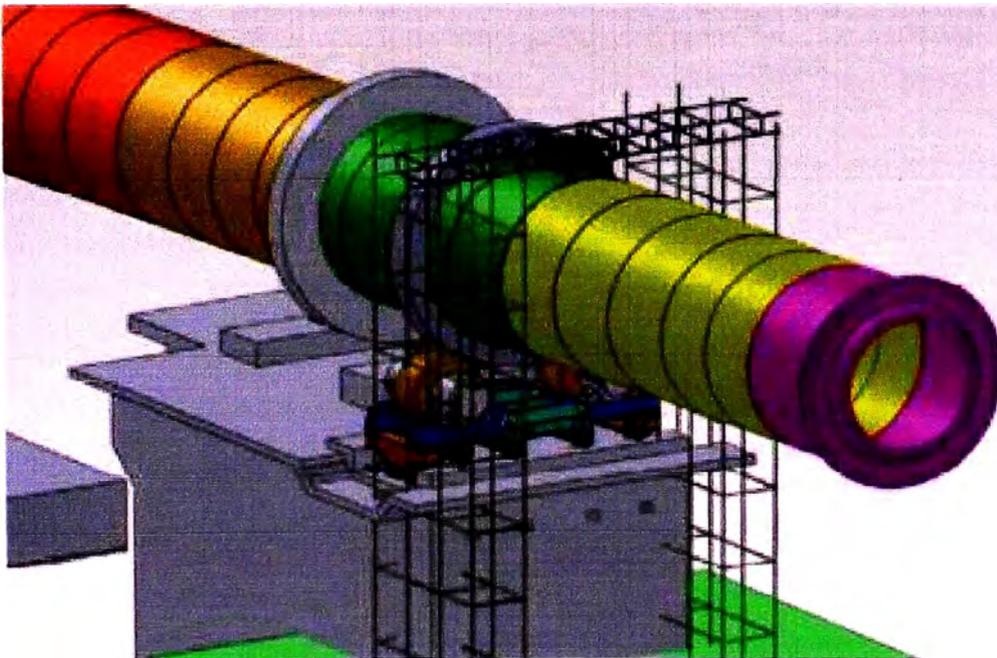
Andamiaje y estructura para la soldadura de Virolas Lado Exterior
